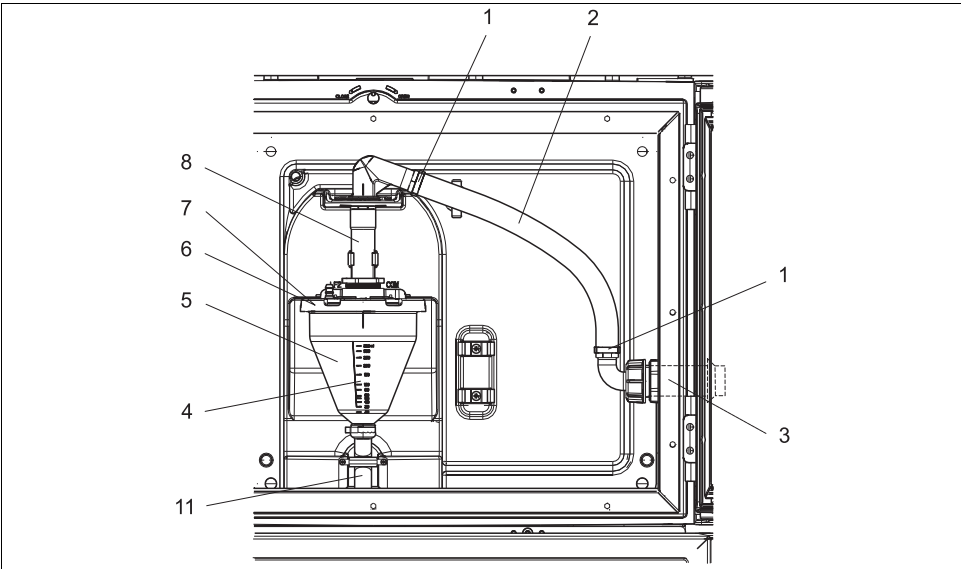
Ersatzteile für Ausführung mit Membranpumpe (Ansicht vor der Pumpenhalterung)
